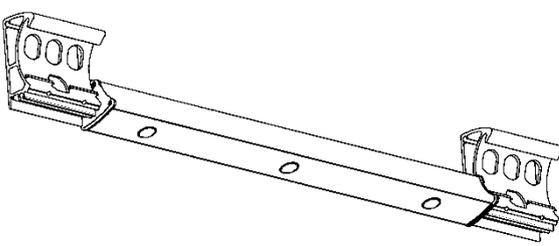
Sondervariante Dachsparrenbefestigung vertauscht mit Dachsparrenhalter und Montageplatte
